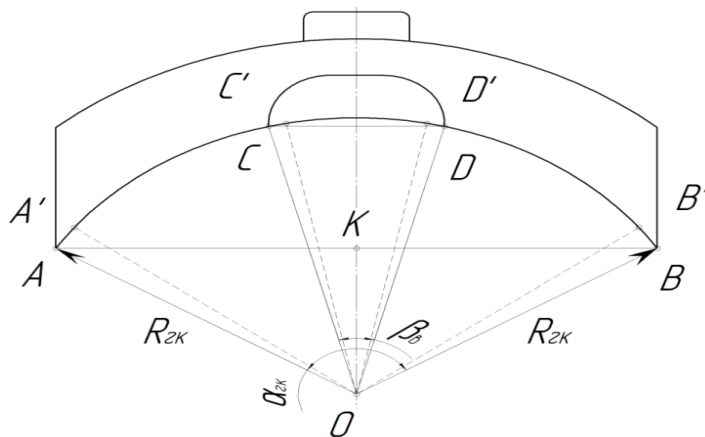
Розрахункова схема КГК типу 2ТР-11:
